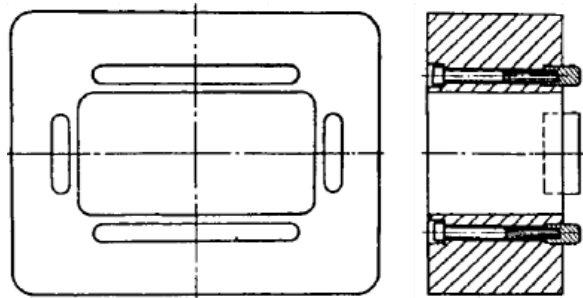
Перетяжні ребра при витяжці коробчастих деталей [3]
